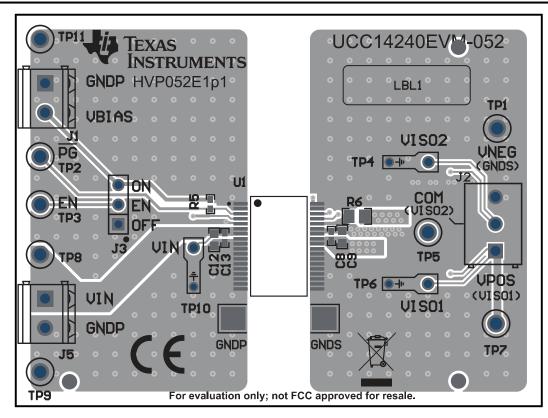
UCC14240EVM-052, PCB Top Layer, Assembly
